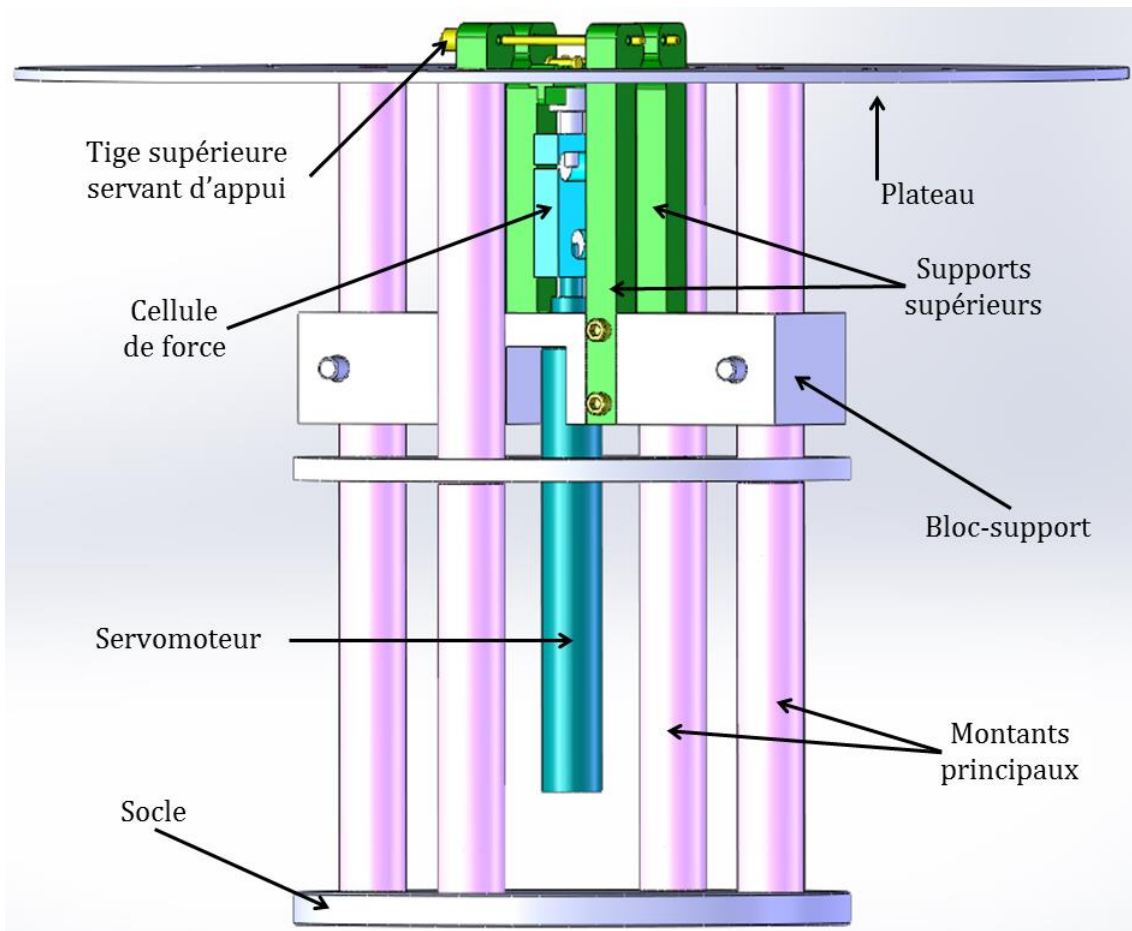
Dessin CAO de la machine de flexion quatre-points : vue 3D de profil.
